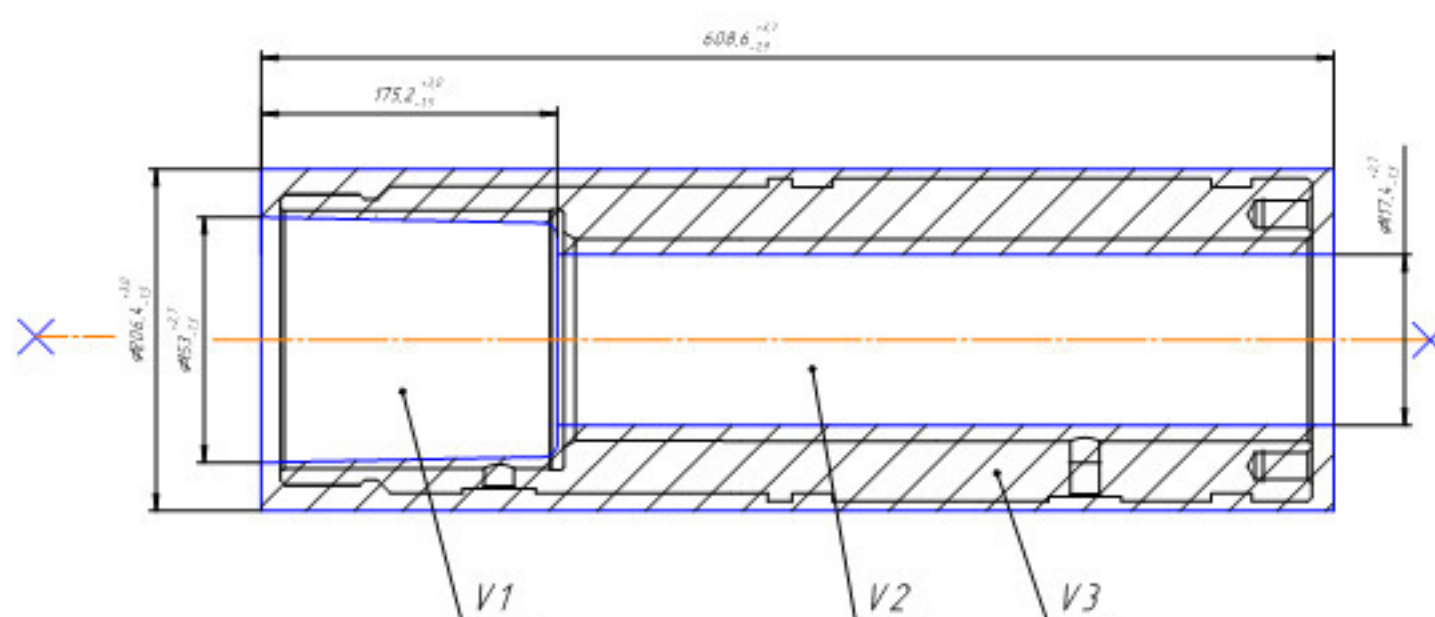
Ескіз заготовки виготовленої на гідравлічному пресі
